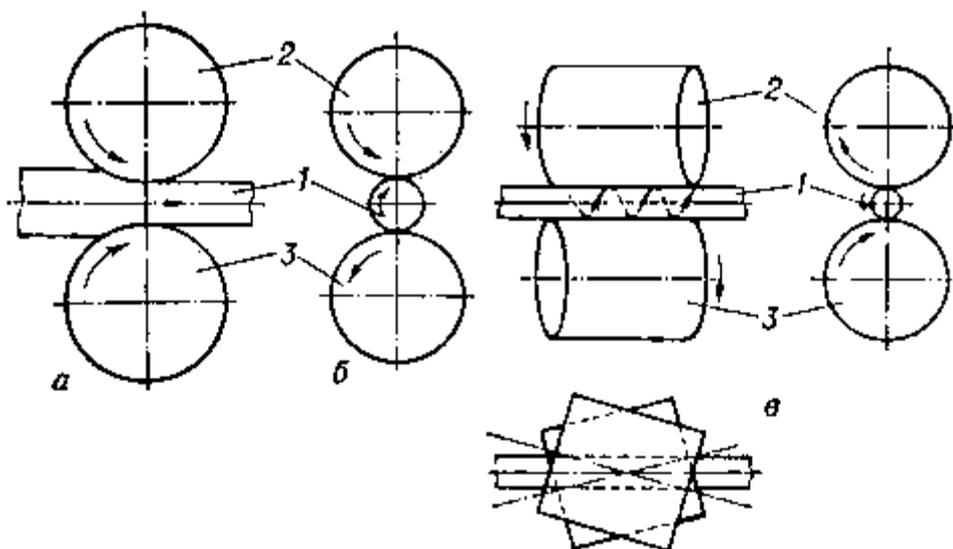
Схема продольной (а), поперечной (б) и винтовой (в) прокатки: 1 — прокатываемый металл; 2 и 3 — валки.
